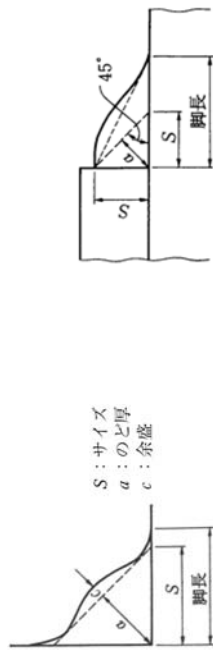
溶接のサイズ 図-解 9.2.7 不等脚の場合の溶接のサイズ
